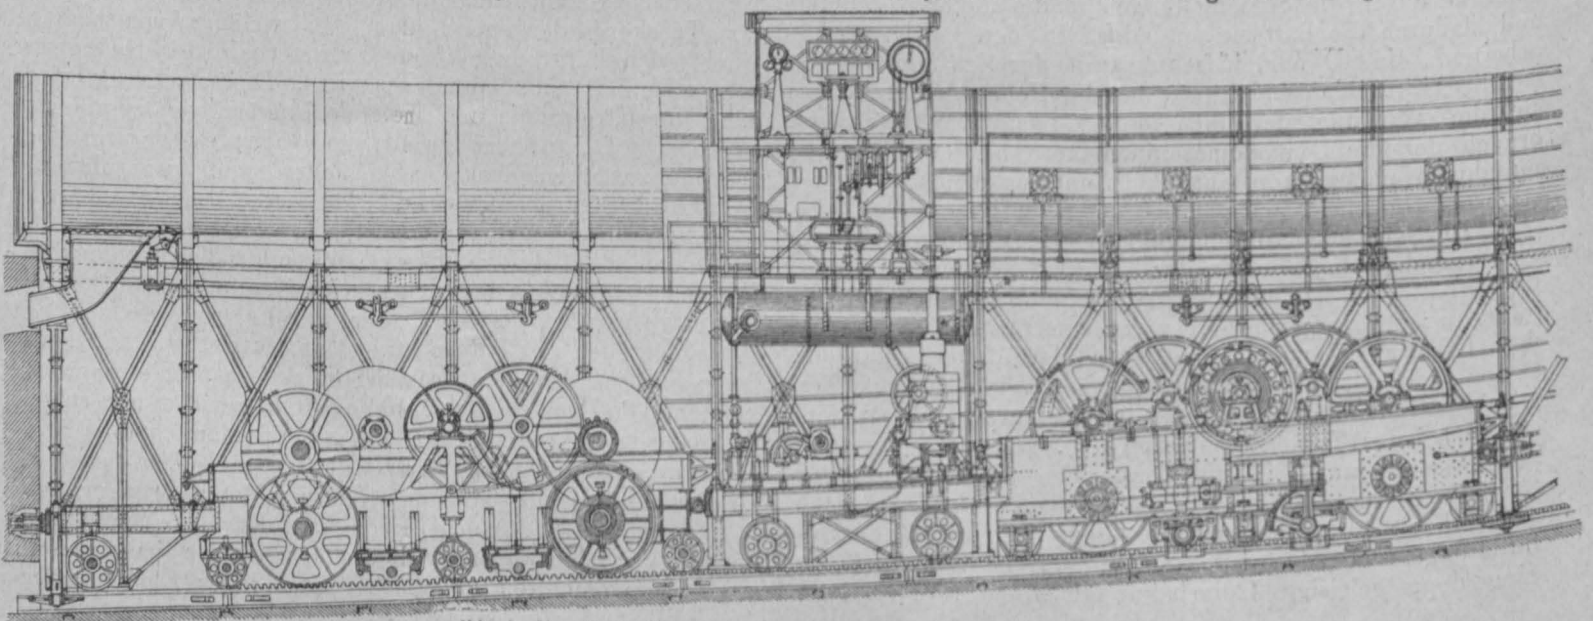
Maschinelle Einrichtung der Motorwagen und des Schiffswagens.
